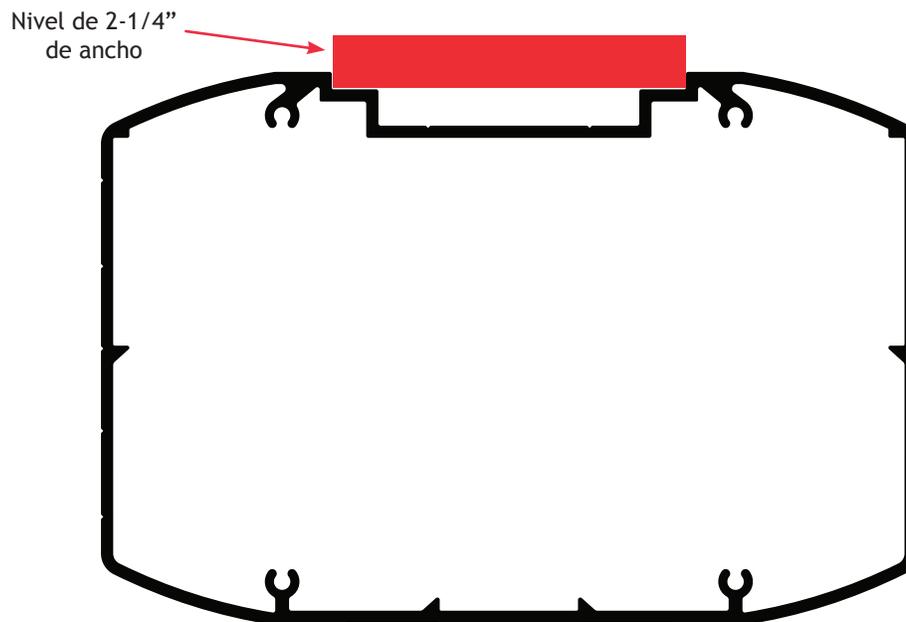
Vista frontal de nivel y canal en el perfil A para alineamiento horizontal
